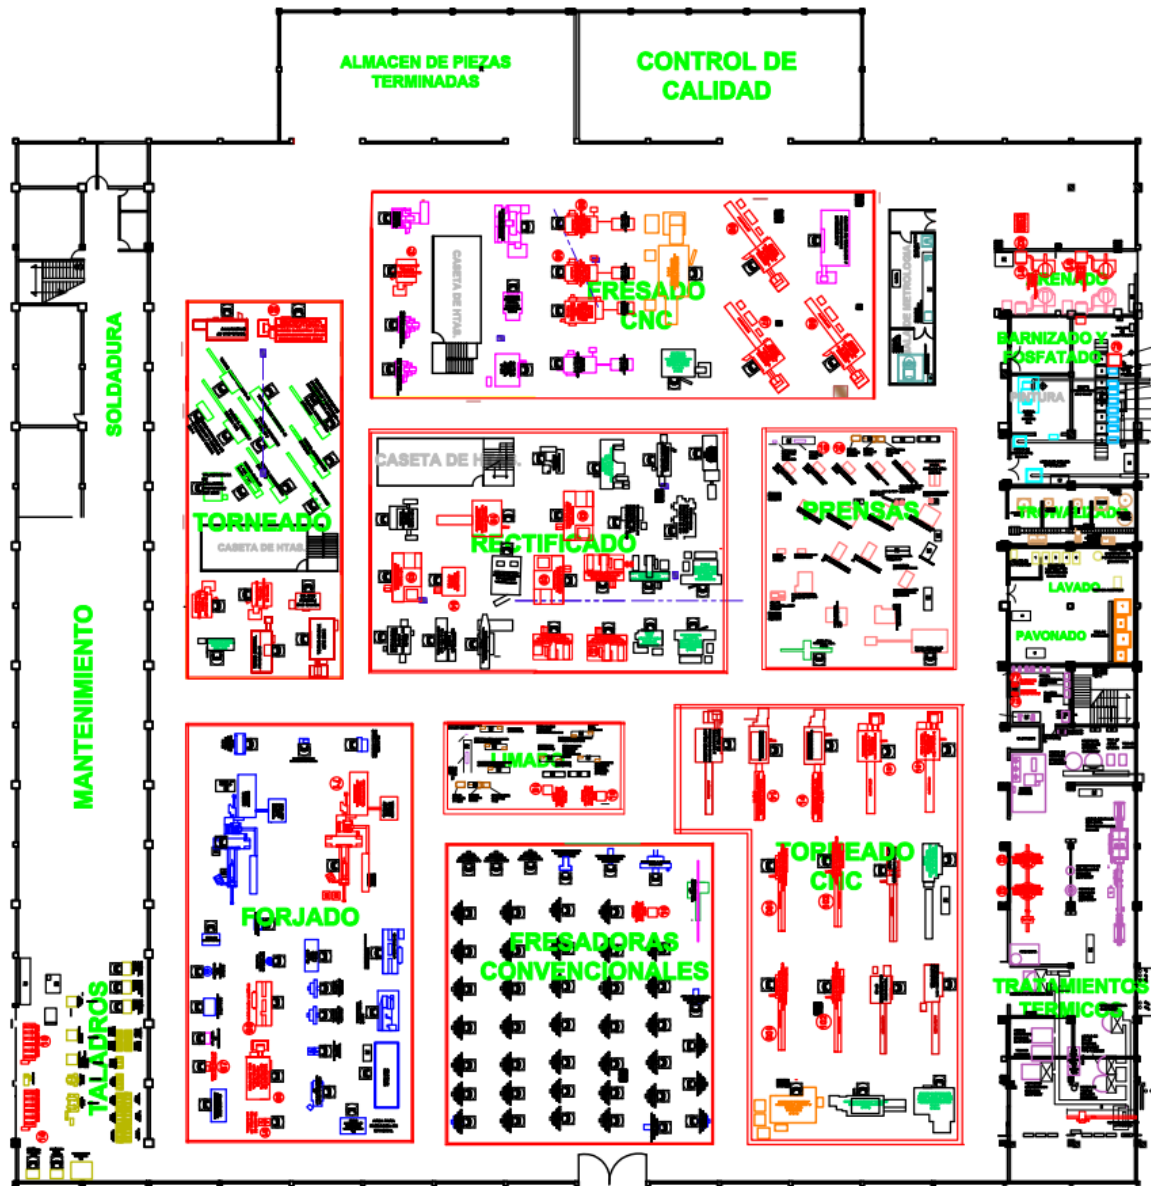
Distribución de planta propuesta para la fábrica de refacciones para armamento. Fuente: Elaboración propia (2018).
